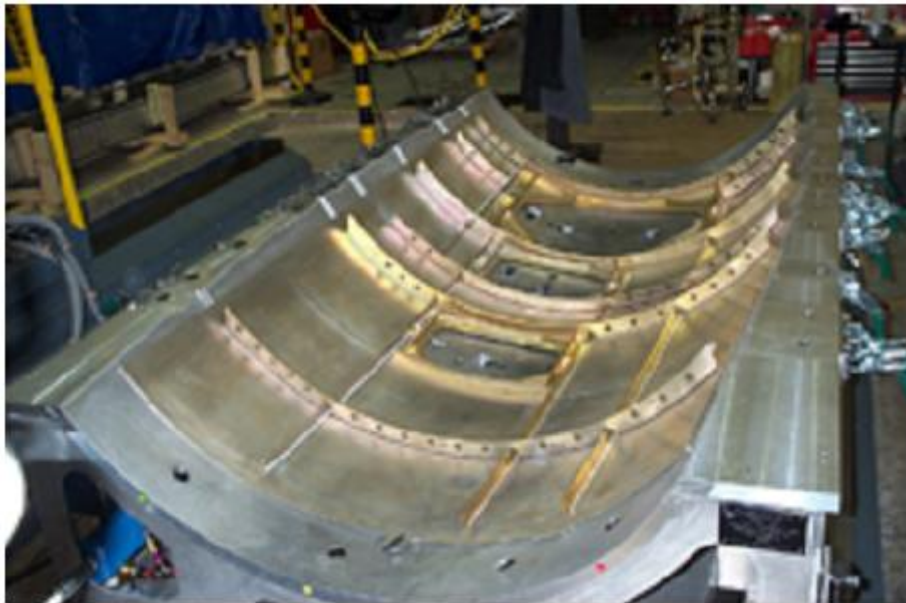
Voilure d'avion soudée par FSW [Tongne.17].
